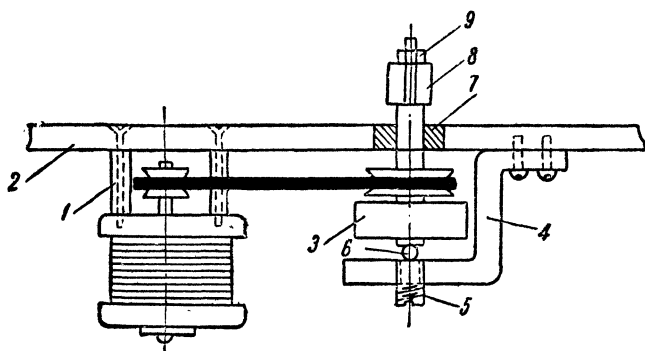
Передача вращения от двигателя к ведущему ролику шкивами и бесконечным ремнем: 1 — колонки для крепления двигателя; 2 — плата механизма; 3 — маховик; 4 — кронштейн маховика (толщина материала 5—8 мм); 5 — регулируемый подпятник; 6 — упорный стальной шарик; 7 — подшипник; 8 — ведущий ролик; 9 — гайка для крепления ролика
